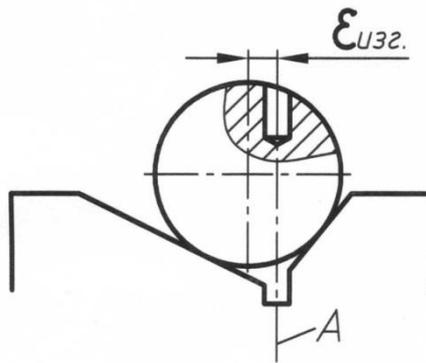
Пример погрешностей, возникающих при изготовлении приспособления
